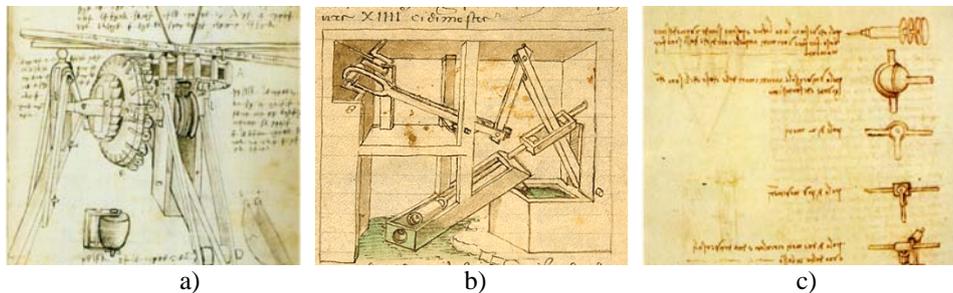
Esempi di primi studi e progetti di macchine del Rinascimento: a) trasmissione ad ingranaggi per gru; b) meccanismo per pompa; c) classificazione di elementi di macchine.
